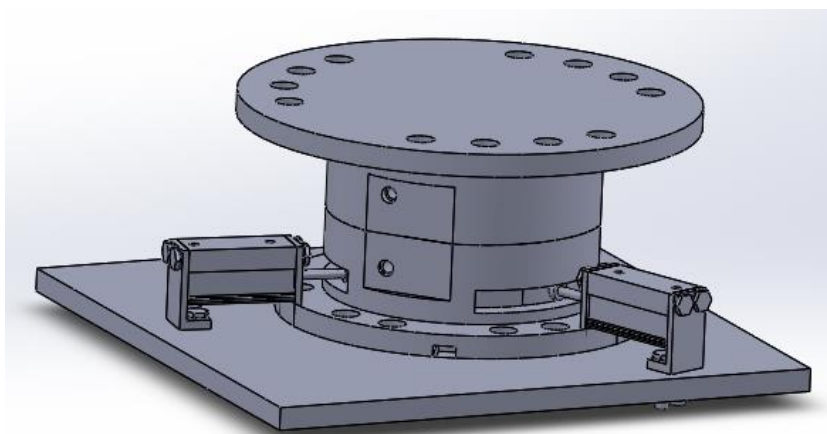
Acoplamiento del plato master y el plato tool con expulsión de los vástagos.
